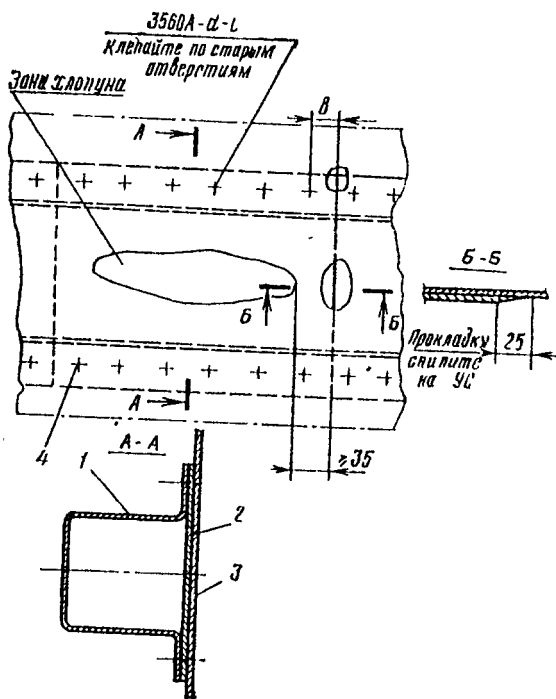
Установка внутренней прокладки для устранения хлопуна:
